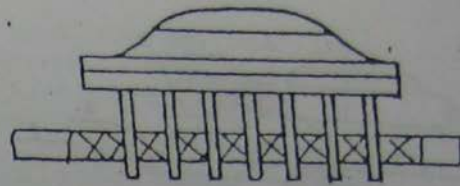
Установка ИМС со штыревыми выводами на печатной плате
